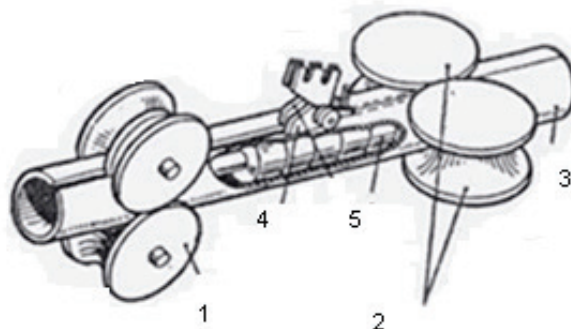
Принципиальное устройство узла сварки трубосварочного агрегата. 1, 2 — обжимные ролики, 3 — трубная заготовка, 4, 5 — ферритовый сердечник в сборе
